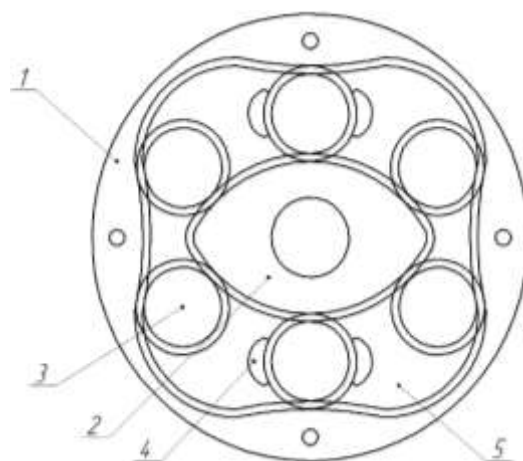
Схема планетарно-роторного гидромотора, рассматриваемая Ан И-Каном:
